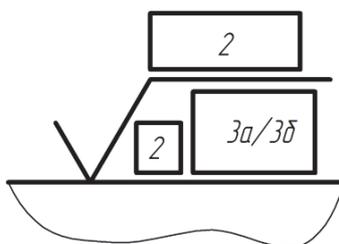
Структура знака для обозначения шероховатости поверхности:
